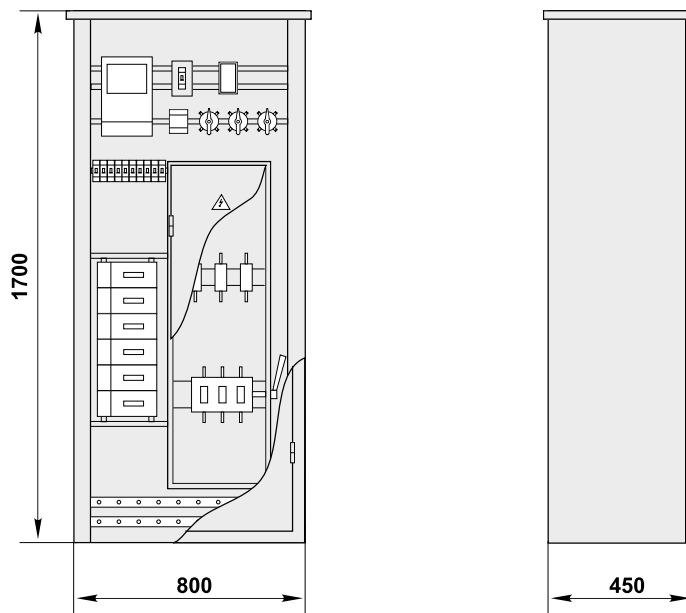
Габаритные размеры устройства ШВУ-5
